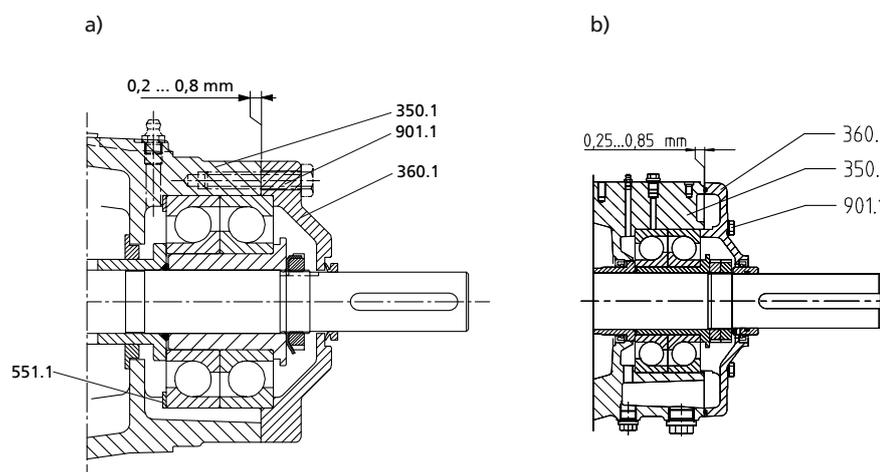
подшипники с консистентной смазкой: а) типоразмер 32-200 и б) типоразмер 250
